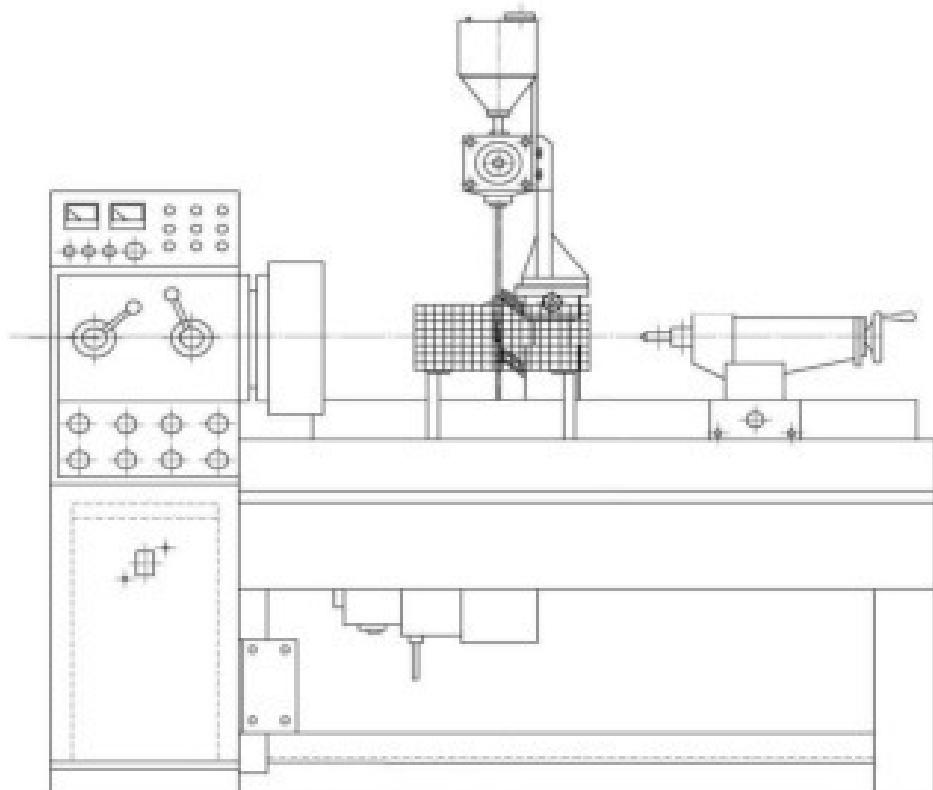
Наплавочный станок УД-209 с защитным ограждением
